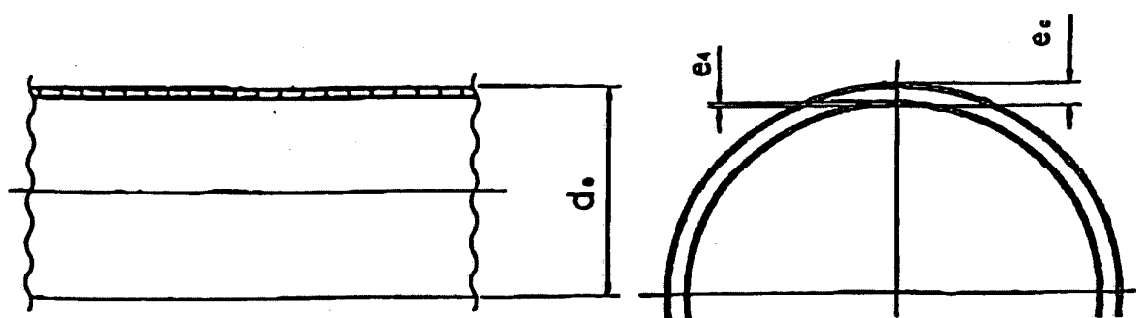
Beispielhafte Ausführung einer Wandkonstruktion, Rohrtyp A2
